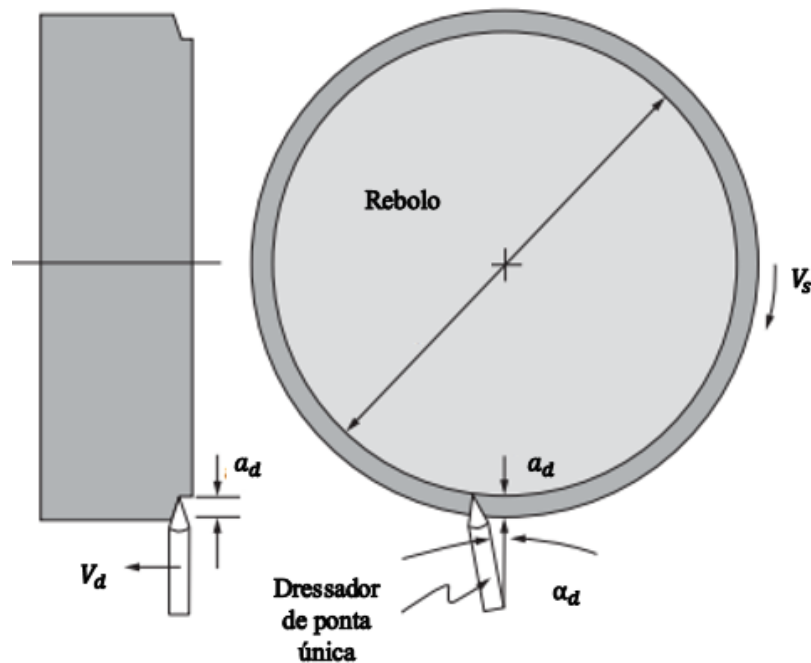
Esquema de dressagem de rebolo com dressador de ponta única (MALKIN; GUO, 2008).
